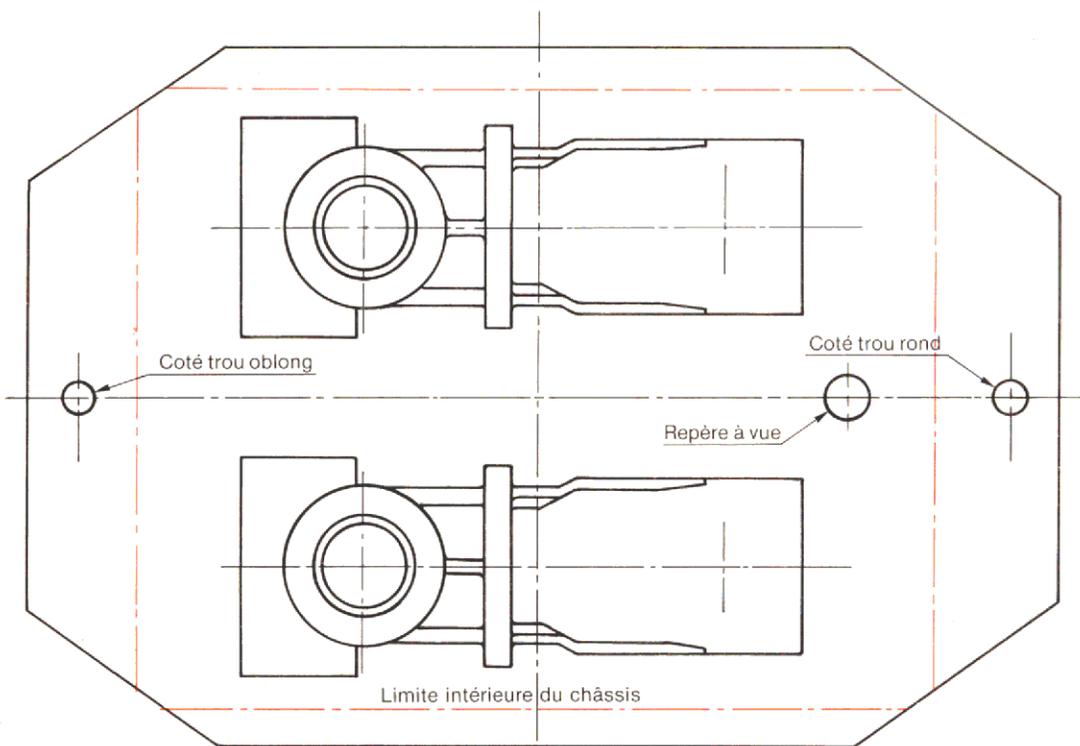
Plaque modèle pour châssis de dessous.
